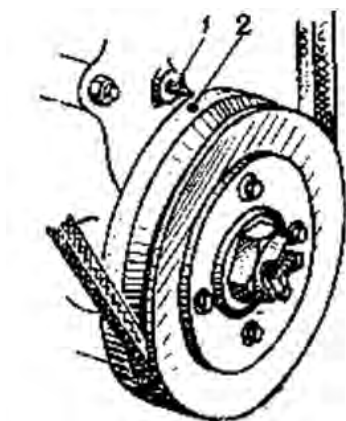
Метка на шкиве коленчатого вала двигателя УМЗ-451 (УАЗ):
